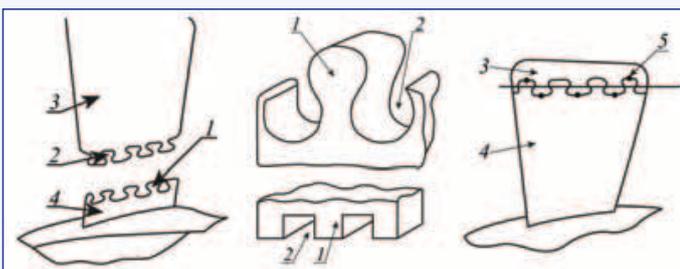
Схема ремонта крыльчаток ротора: 1 - профильные шипы; 2 - профильные пазы; 3 - сменная лопатка; 4 - основание лопатки; 5 - прихватки
